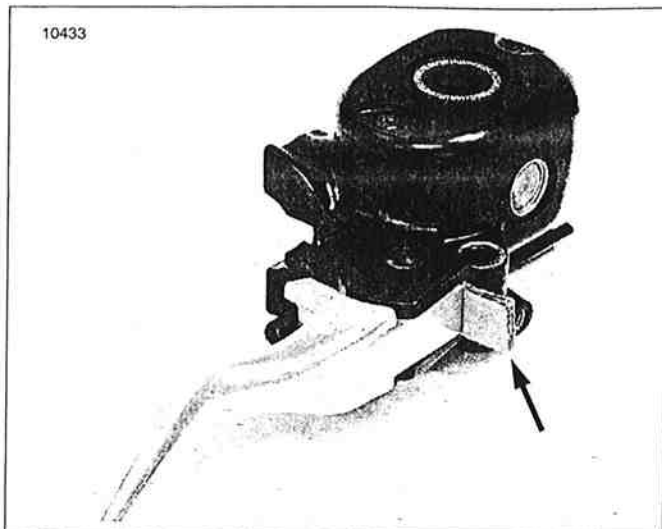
Instalación del inserto de cartón de 4 mm (5/32 pulg.) antes de instalar el conjunto de la bomba de frenos
